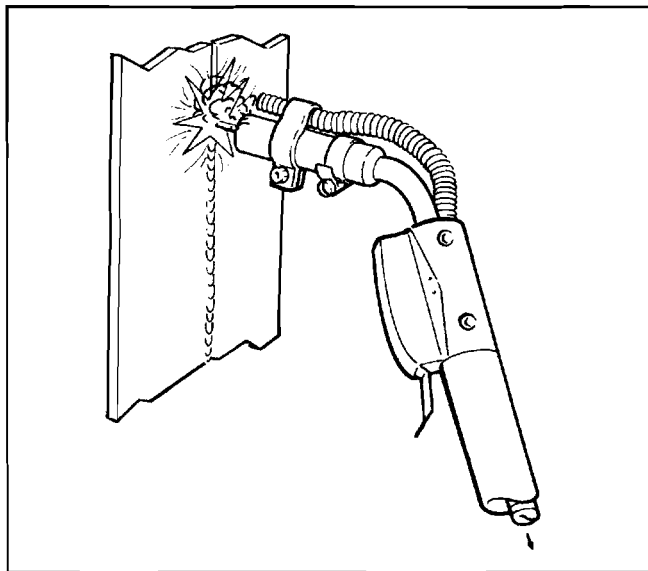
PISTOLA DE SOLDEO CON EXTRACTOR
